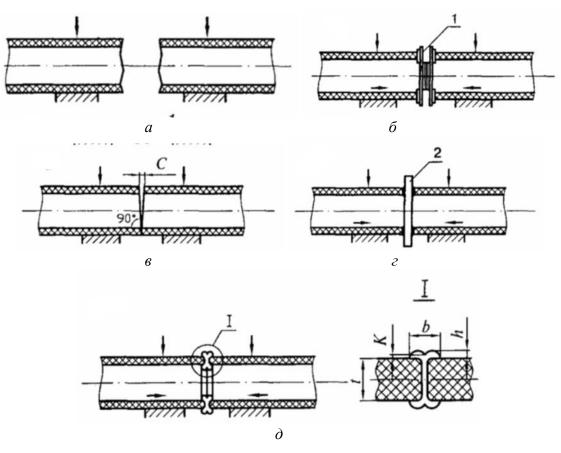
Последовательность процесса сборки и сварки встык труб из полиэтилена: a — центровка и закрепление в зажимах сварочной машины концов свариваемых труб;  $\delta$  — механическая обработка торцов труб с помощью торцовки 7;  $\epsilon$  — проверка соосности и точности совпадения торцов по величине зазора C;  $\epsilon$  — оплавление и нагрев свариваемых поверхностей нагретым инструментом 2;  $\delta$  — осадка стыка до образования сварного соединения (в сечении I даны буквенные обозначения основных геометрических размеров соединения встык)
